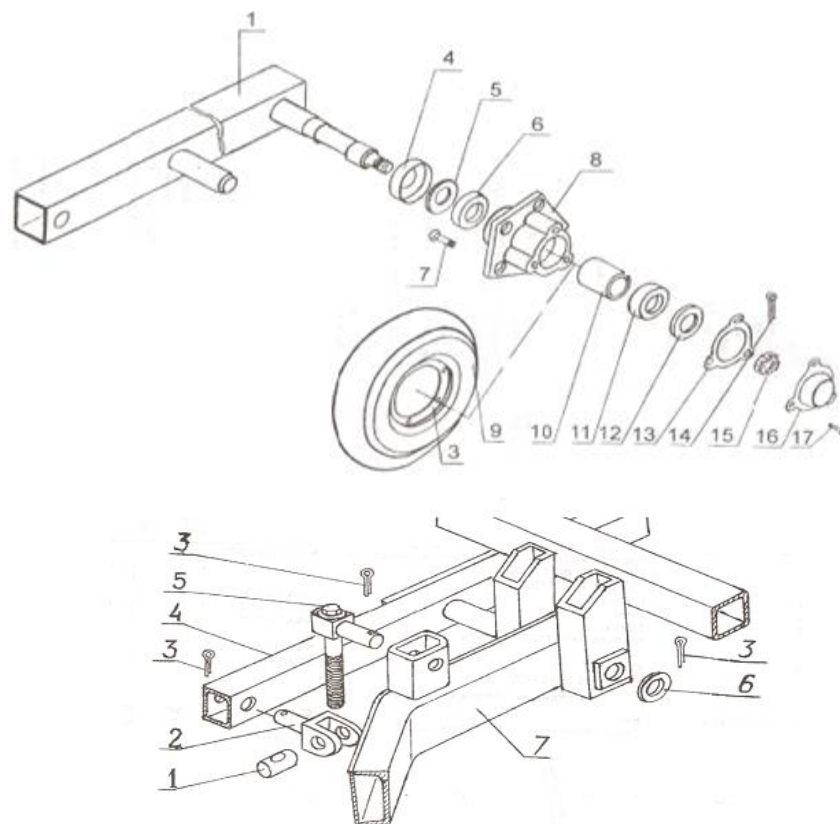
Конструкція ходової частини культиватора КПС-4.
